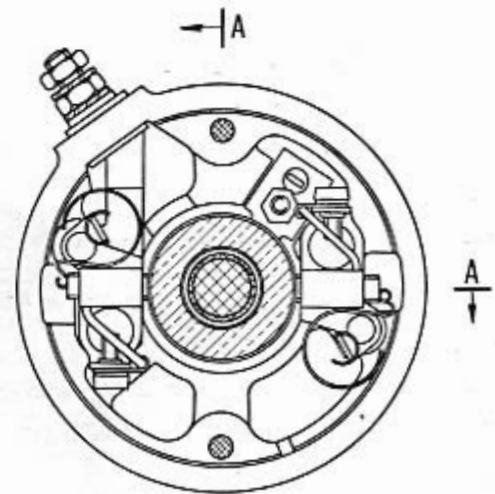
Coupe transversale de la dynamo et vue du palier côté collecteur.
